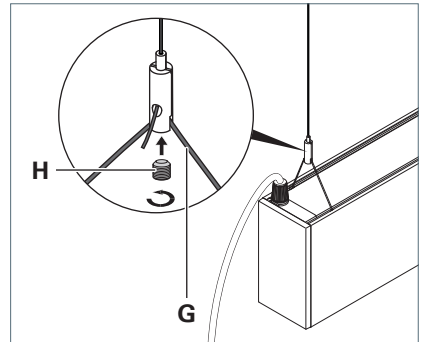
Leuchte an Drahtseilhalter befestigen.
